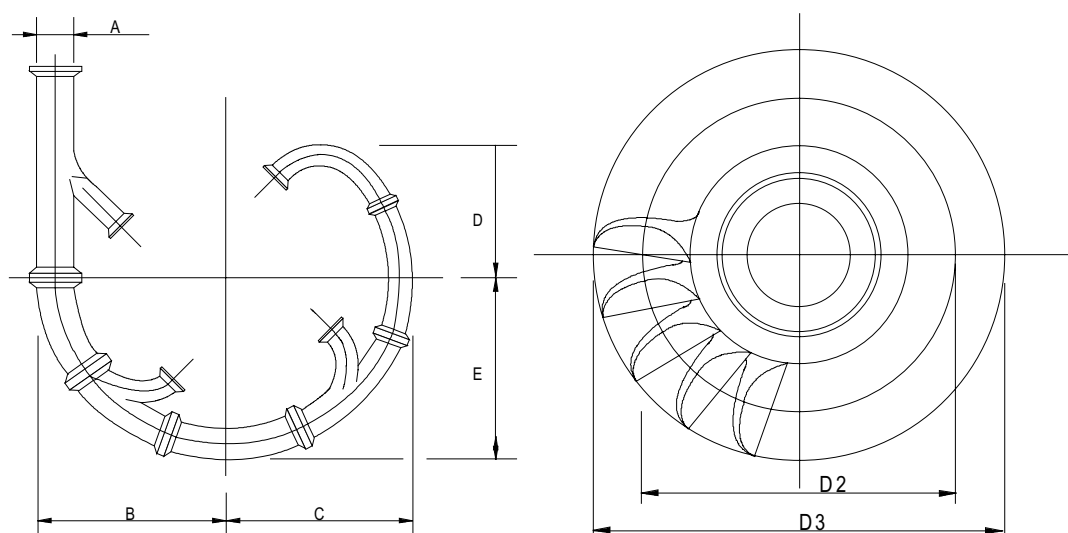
Planta dos bicos injetores e rotor – Turbina Pelton.
